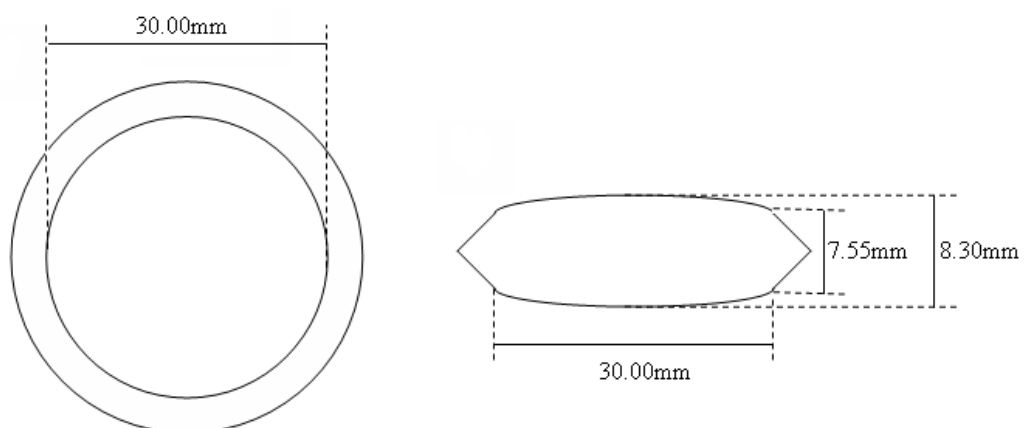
Abmessungen der gestauchten Ni-Scheibe in Draufsicht (links) und Querschnitt(rechts)
